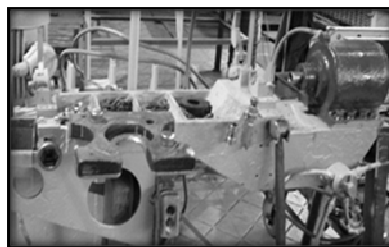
, б – Пресс для напрессовки шестерни распределительного вала
